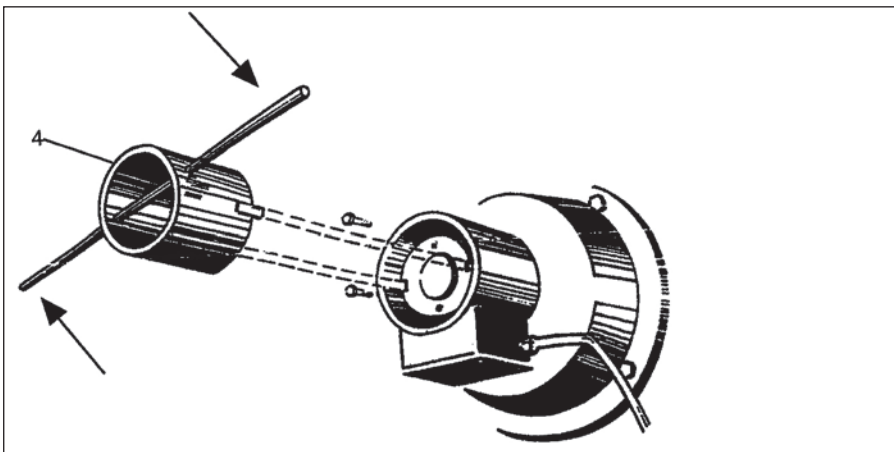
Отпуск аварийного тормоза (захватывающего устройства).
